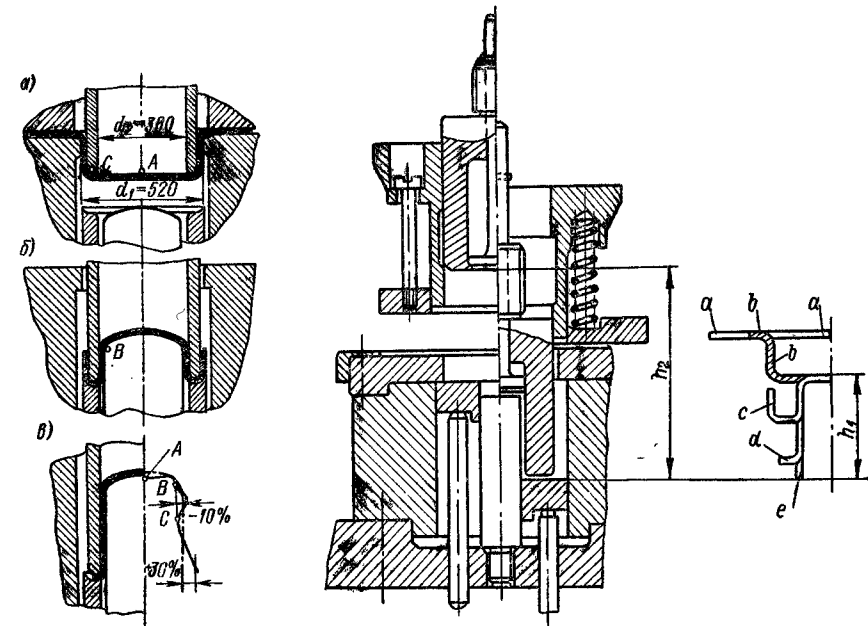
Процесс реверсивной вытяжки (с выворачиванием)
